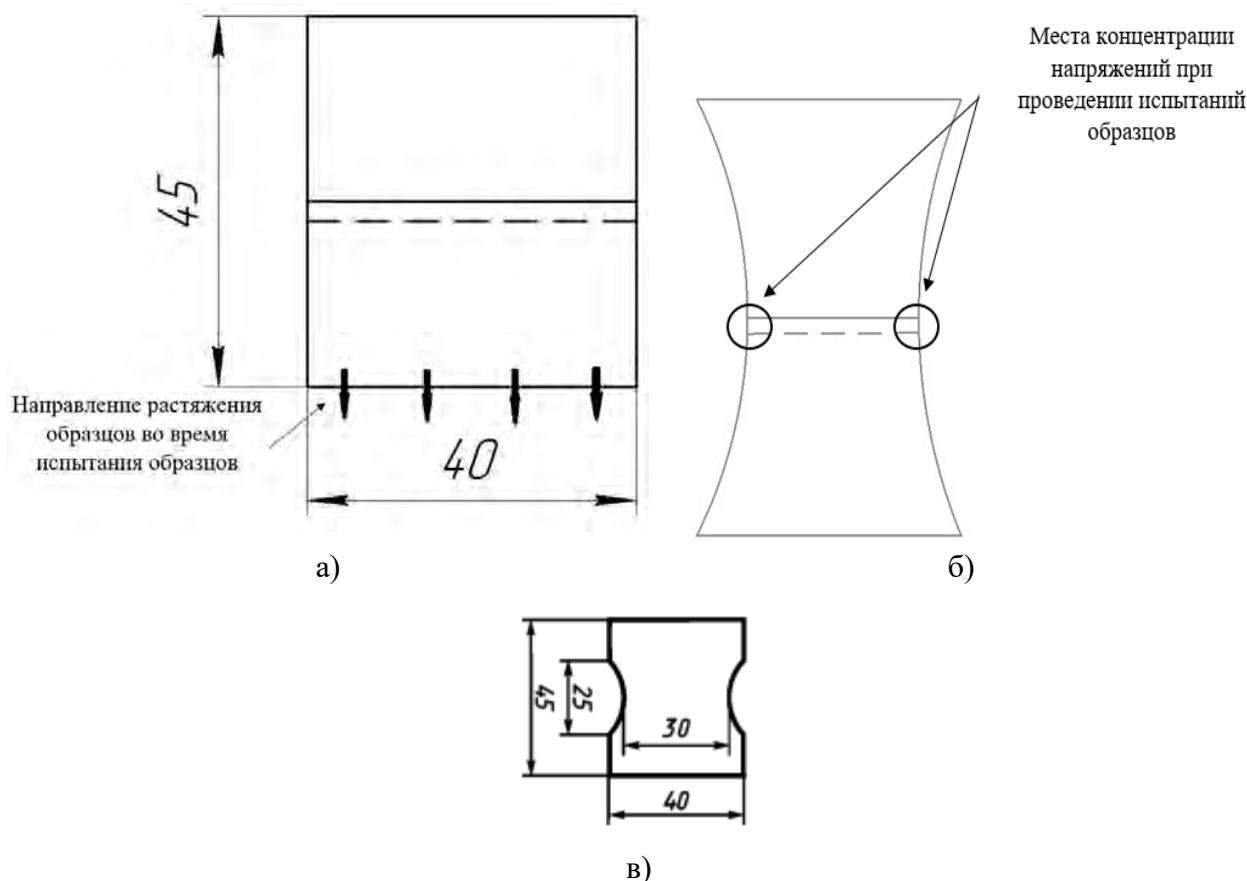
Формы образцов для испытаний ниточных соединений по ГОСТ 9290: а) форма образца, выкроенного из готовой обуви; б) внешний вид образца в процессе испытания; в) форма непростроченных образцов
